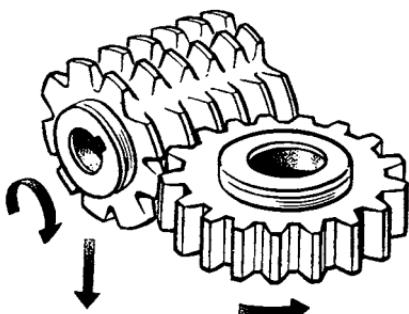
Схема фрезерования зубчатого колеса червячной фрезой.
